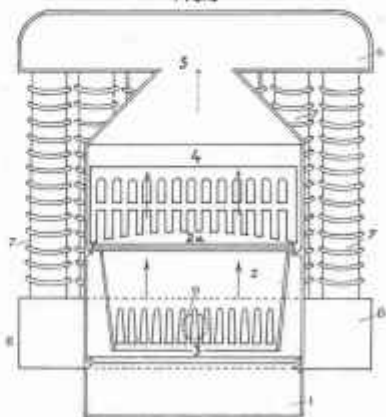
FIG. I. — COUPE LATÉRALE DE L'ENSEMBLE DU DISPOSITIF BREVETÉ
